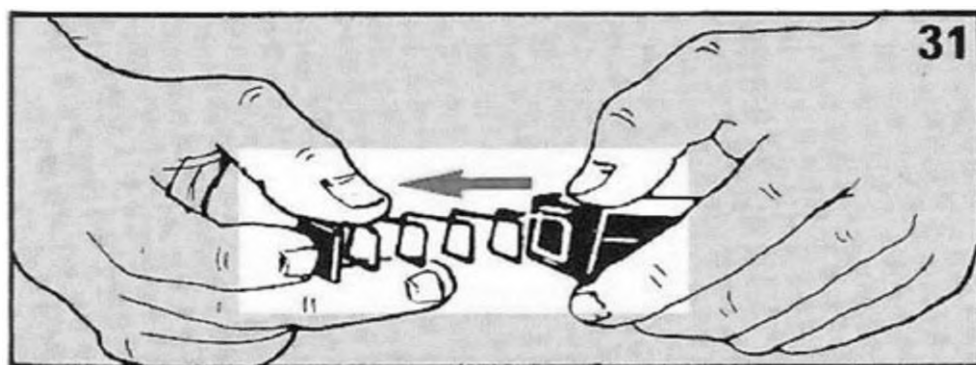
Порядок вилучення пружини із корпусу магазину
